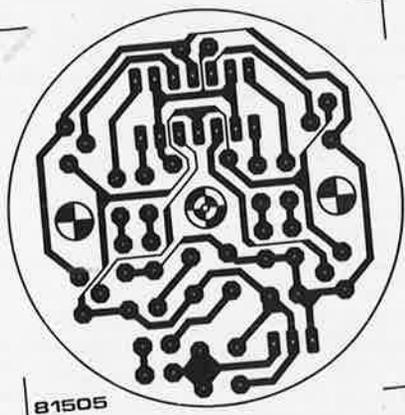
Le dessin du circuit imprimé a été conçu de celle sorte qu'il s'adapte aux boîtes de conserve. D7, la LDR et le câblage sont soudés côté cuivre.
